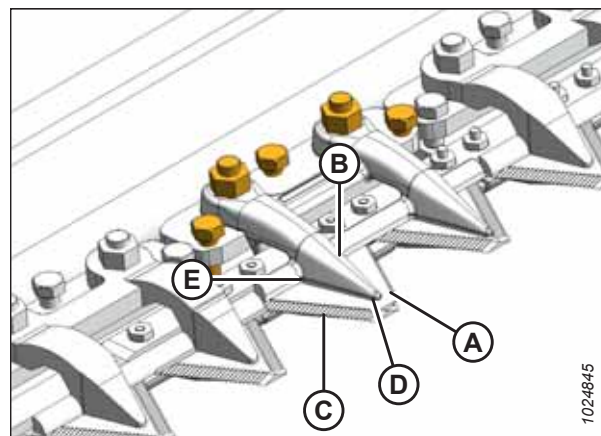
Rabatteur du doigt de lamier court central sur couteau double
